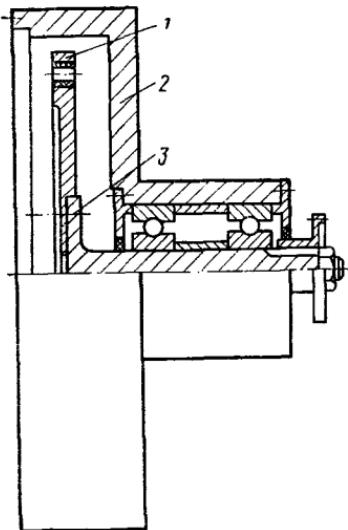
Переходник для установки и закрепления гидромеханической передачи на стенде:
